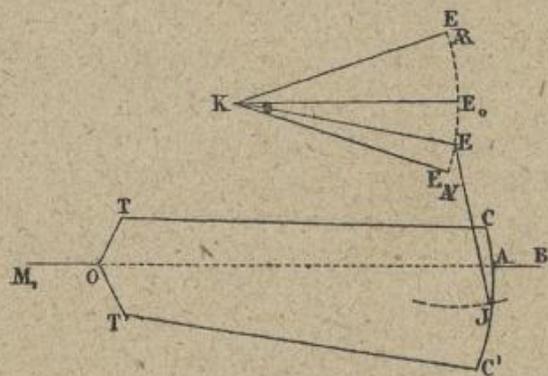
Tiroir conduit par un point intermédiaire de la coulisse.
